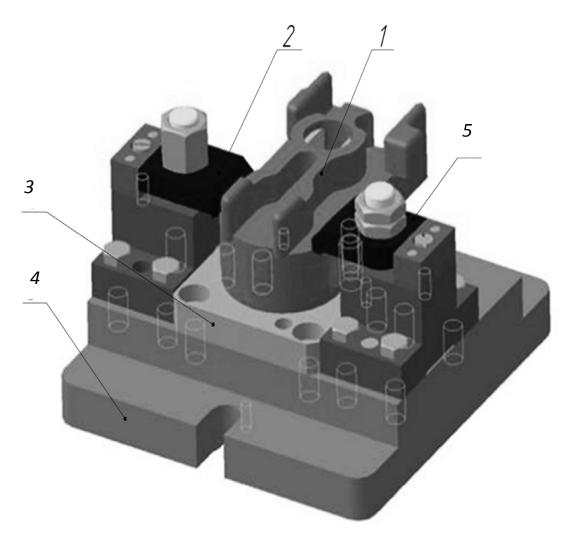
3D-модель общего вида станочного приспособления для фрезерования детали «Корпус»: 1- заготовка; 2, 5- прихваты; 3- плита; 4- основание
